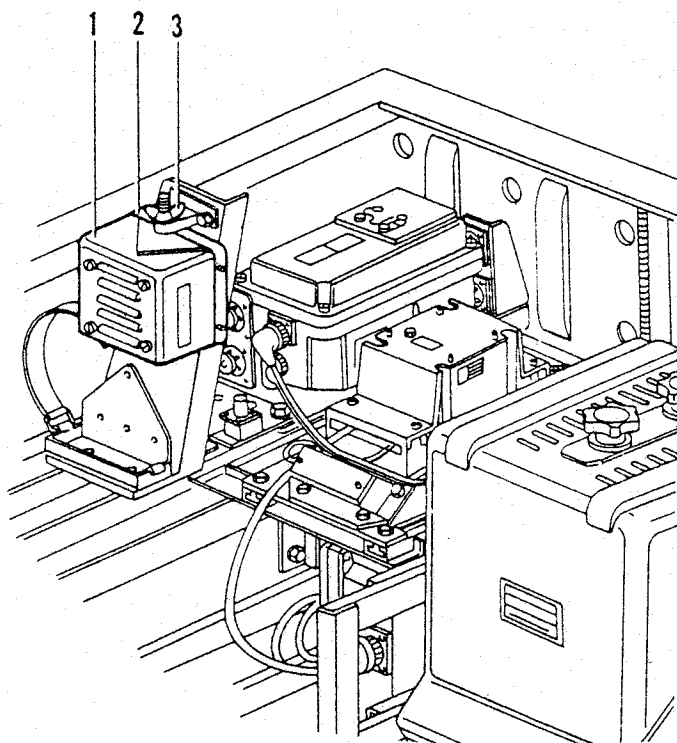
Befestigung des Lautsprechers im Fahrzeugheck
